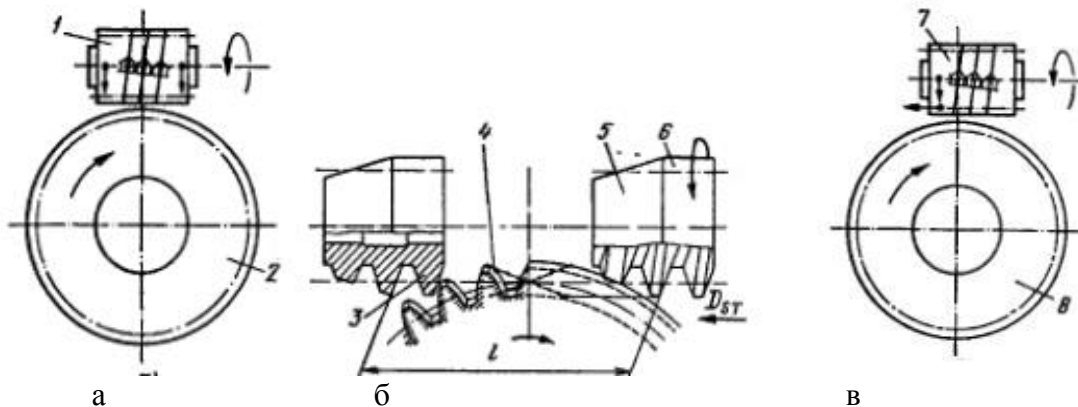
Схеми фрезерування зубів черв'ячного колеса черв'ячними модульними фрезами
